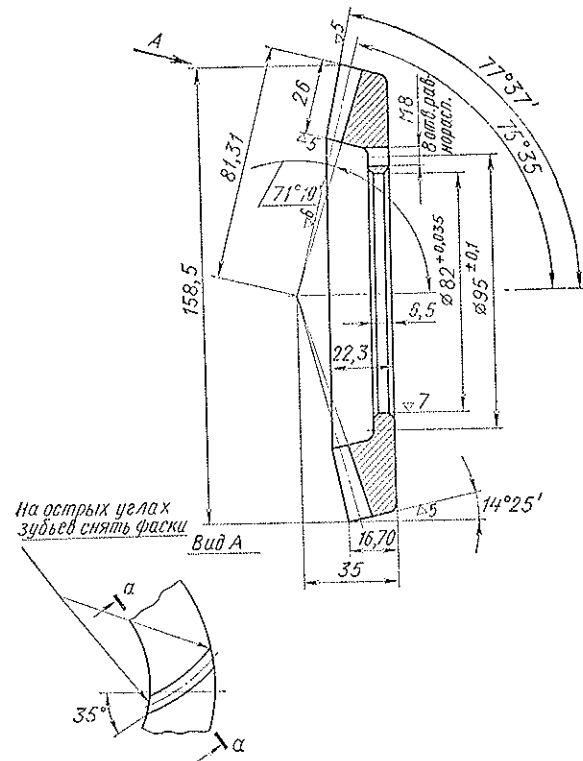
Ведомая шестерня, применяемая с коробкой № 2. Данные для изготовления: число зубьев — 35; модуль торцевой — 4,5; тип зубьев — круговые; угол профиля исходного контура — 20°; угол спирали — 35°; направление спирали — левое; диаметр режущей головки — 6R¹¹; полная высота зуба у торца — 8,28; коэффициент смещения исходного контура — 0,46; степень точности — 7. Данные для измерения: измерительные размеры зуба в сечении а-а; высота — 2,31. Данные для справок: толщина зуба по дуге делительной окружности — 4,95; коэффициент тангенциальной коррекции — 0,16; высота головки зуба — 2; форма зуба 1.
